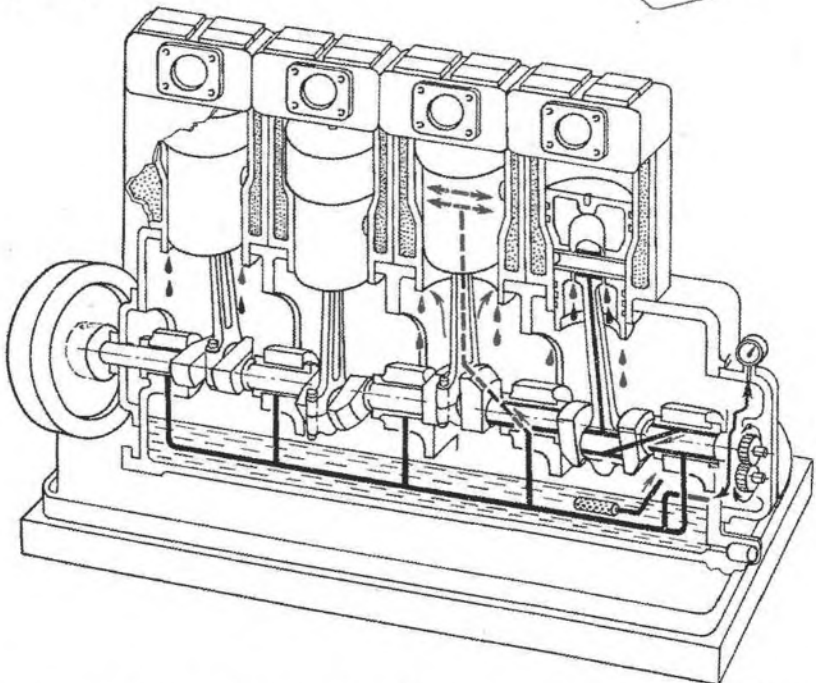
Смазка механизма движения под давлением, а цилиндров — разбрызгиванием
